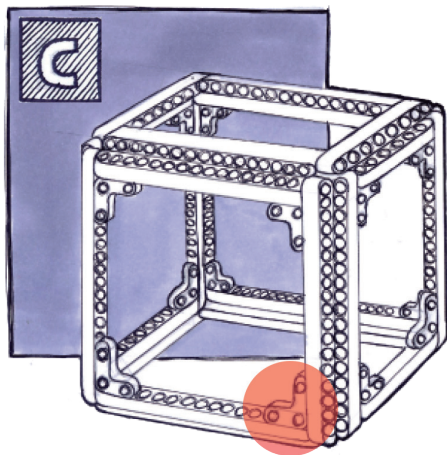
Estructura C: Sistema de construcción Lego technic.
